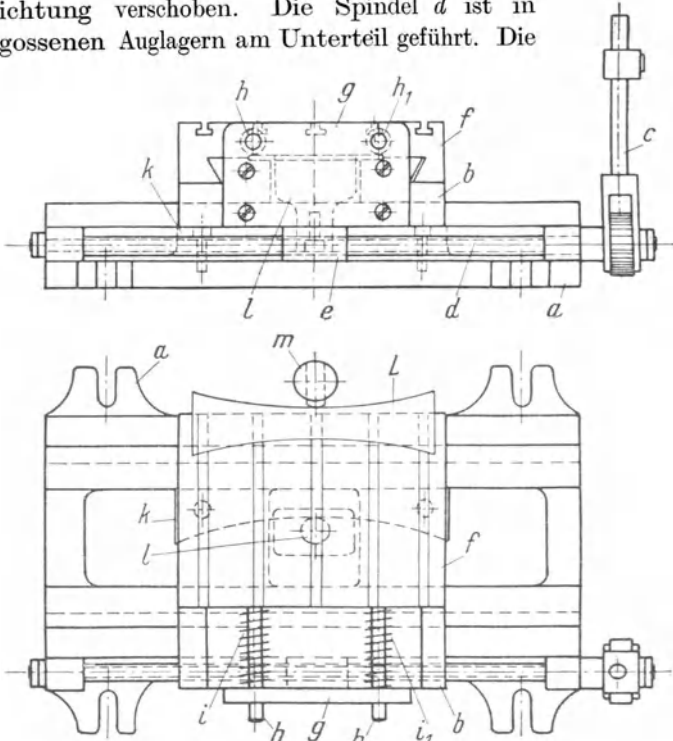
Kopier-Stoßvorrichtung für Fassonstücke.
